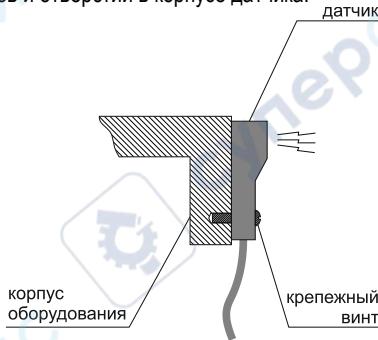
Установка датчика с торцевым расположением чувствительной поверхности
